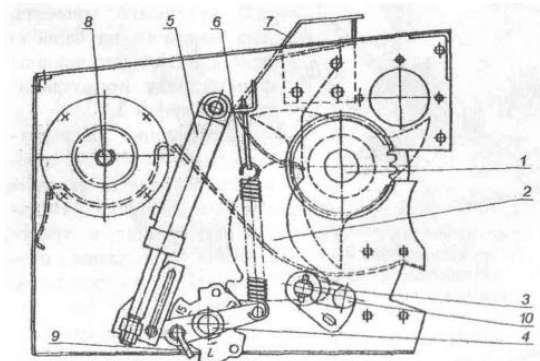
Измельчитель: 1 – подающий барабан; 2 – нож; 3 – ось ножей; 4 – вал; 5 – гидроцилиндр; 6 – пружина; 7 – гребенка; 8 – нижний передний валец; 9 – рычаг; 10 – фиксатор оси ножей
